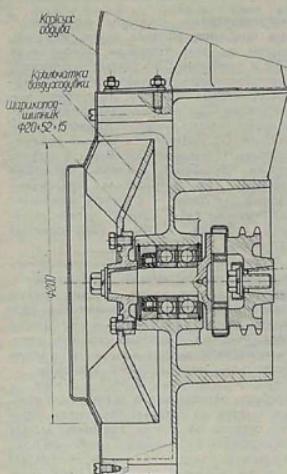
Привод воздуховодки и кожух обдува для двигателя ИЖ-56.
